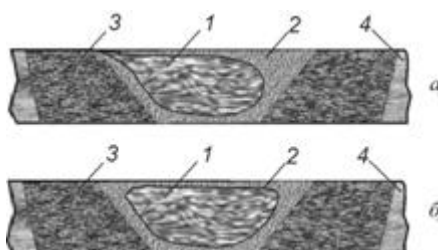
Структура швов, получаемых при ПСТ с однонаправленным вращением инструмента (а) и возвратно-вращательным (б): 1 – «ядро» сварки, перенесенный инструментом термопластически деформированный материал; 2 – зона термопластической деформации; 3 – зона термического влияния; 4 – исходный материал.
